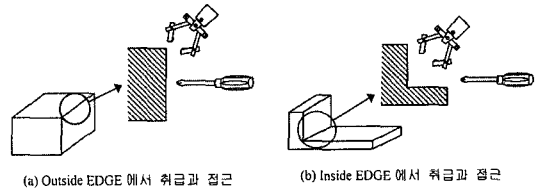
EDGE에서 Robot Arm에 의한 취급과 Tool의 접근
